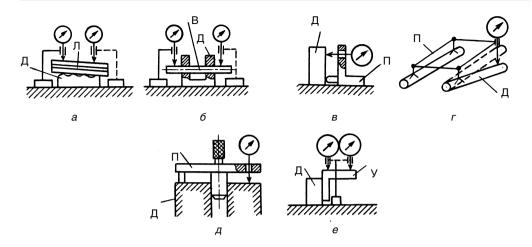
Схемы контроля отклонений расположения с помощью: а — линейки и поверочной плиты; б — валика; в, г, д — специальных приспособлений; е — угольника
